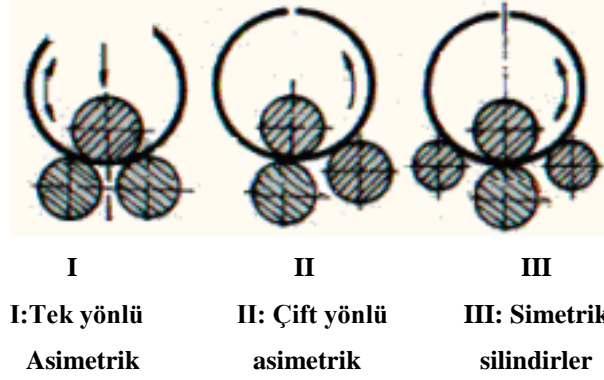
Sac ve yassı gereçlerin büküldüğü silindir makineleri
